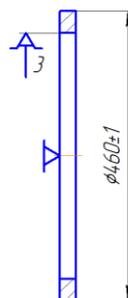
Эскиз базирования заготовки на 005 токарной операции.
